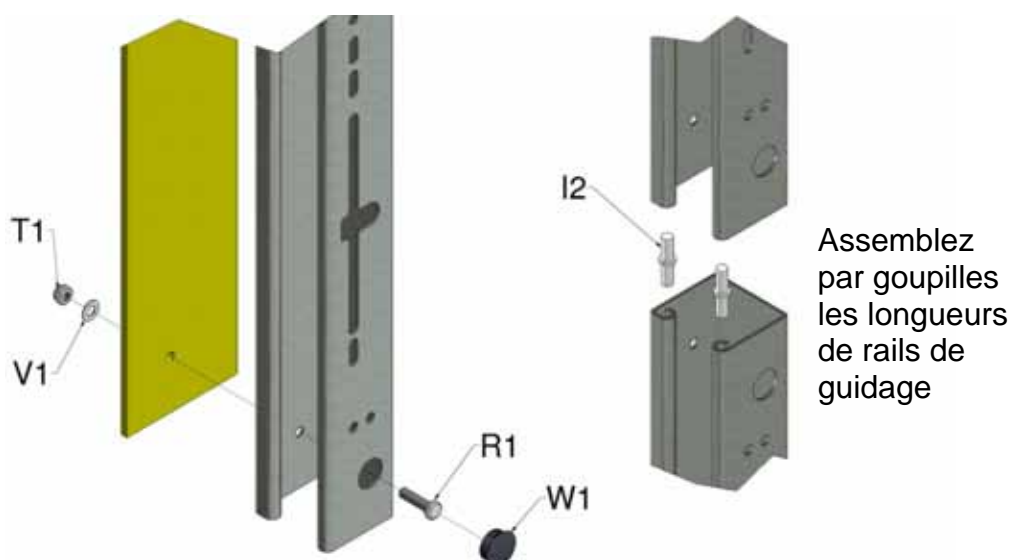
, boulonnage des rails de guidage et assemblage du rail de guidage à la paroi
